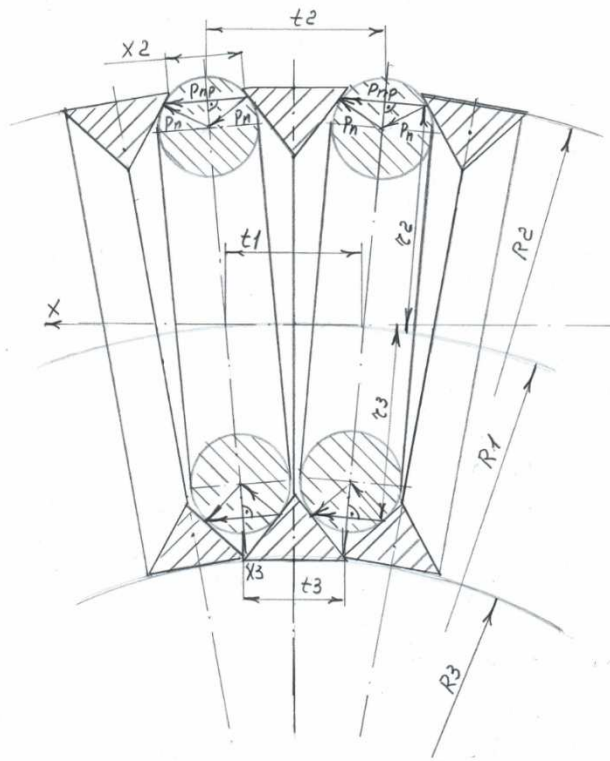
Конструктивна схема вигнутої частини гнучкої стійки
